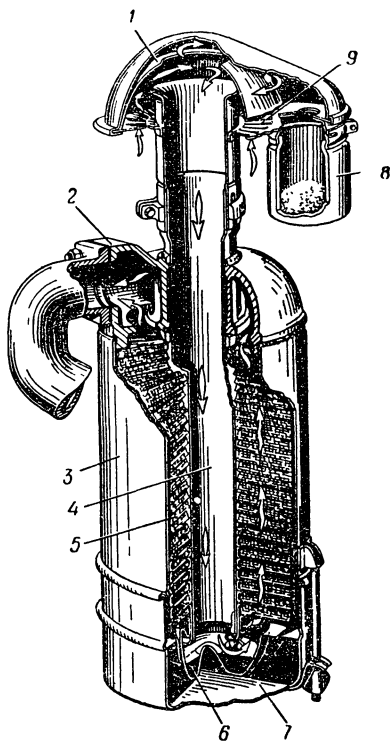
Воздухоочиститель дизеля КДМ-46:
